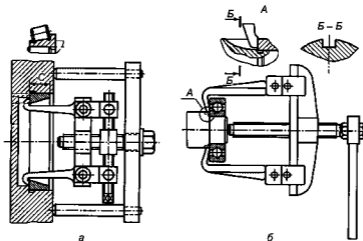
Установка винтового съемника: а – при удалении из корпуса; б – при снятии с вала; С – ширина подшипника
